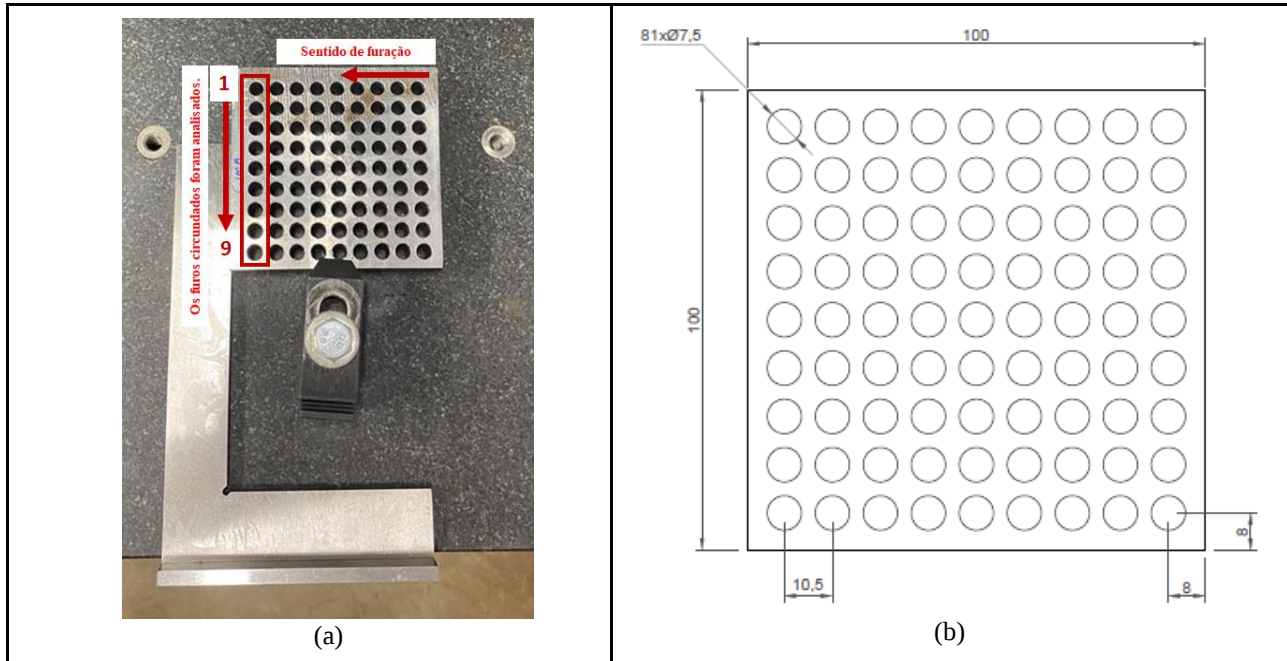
Distribuição dos furos sobre o corpo de prova (a) Montagem na máquina de medição por coordenadas com indicação do sentido de furacão e destaque para os furos inspecionados por medição e (b) Desenho esquemático da distribuição dos furos.
